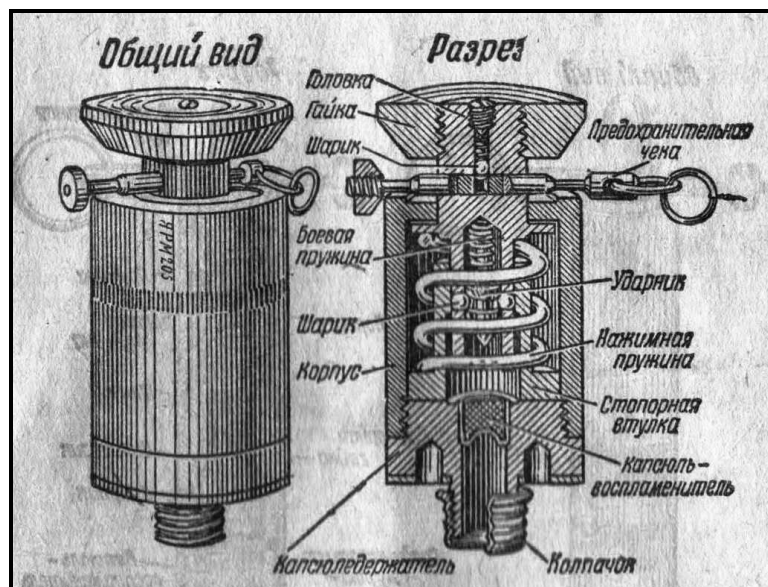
Немецкий взрыватель нажимного действия DZ-35
